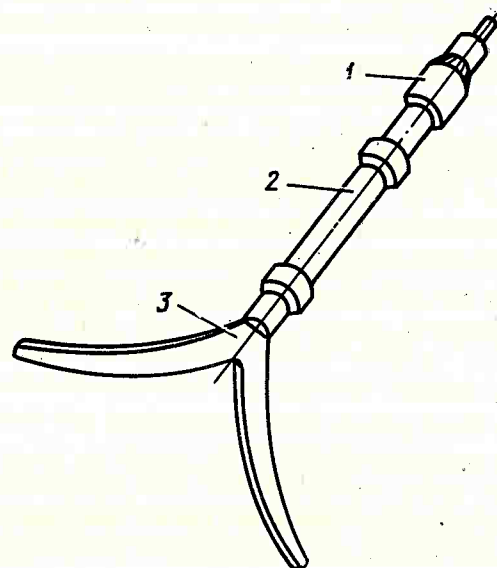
Вилка для центрирования валов гидроагрегатов:
